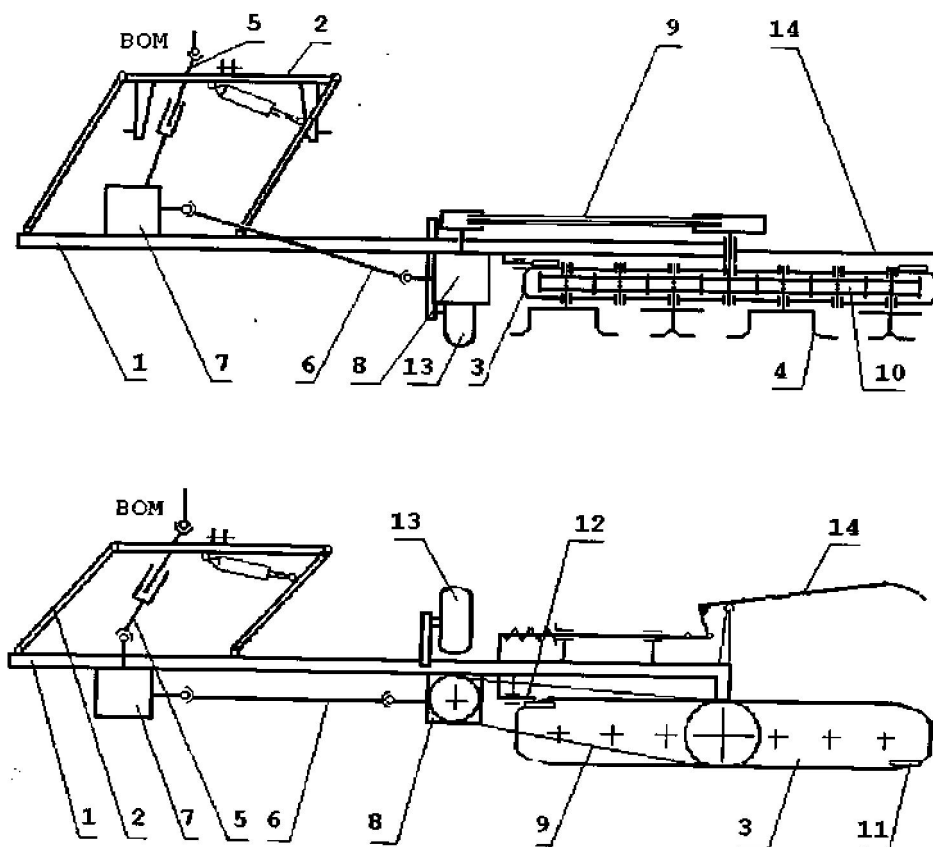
Схема машини МПП-1,2: 1 - рама; 2 - паралелограмний механізм; 3 - корпус; 4 - ротори з ножами; 5, 6 - карданні передачі; 7, 8 - конічні редуктори; 9 - пасова передача; 10 - зубчасті передачі; 11 - упори; 12 - фіксатор; 13 - опорне колесо; 14 - щуп
